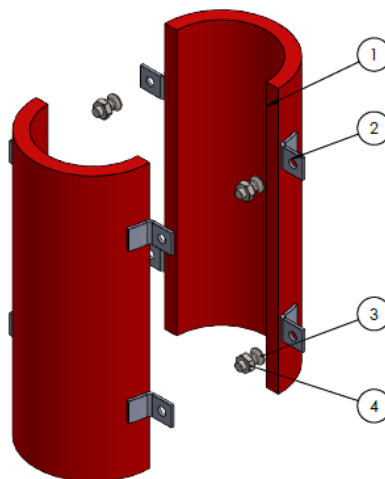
Conjunto Mazo Equipo Plug Maker.
